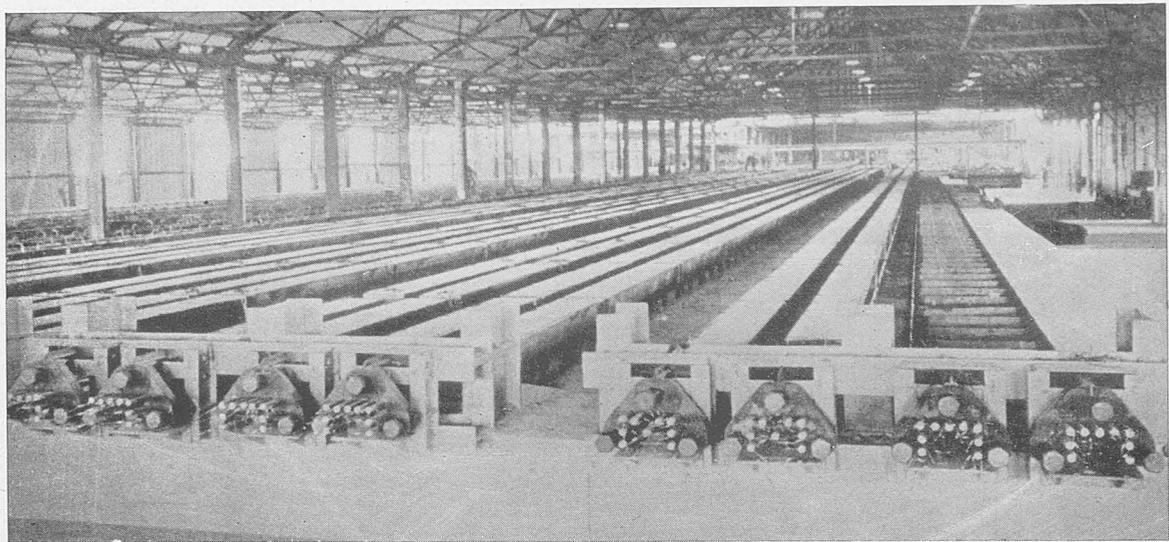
Filas de moldes en serie en una fábrica inglesa de traviesas de hormigón pretensado.
